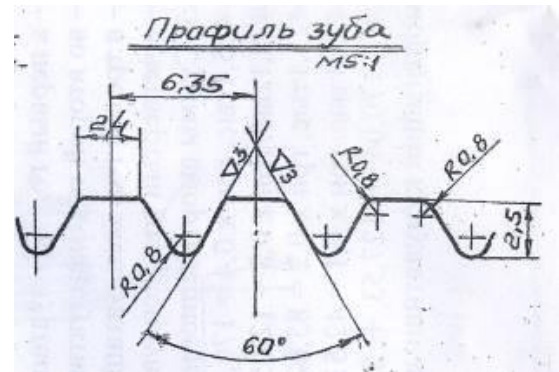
Креслення профілю зуба пили холодного різання / Fig. 1. The arm of the tooth profile drank cold risana
